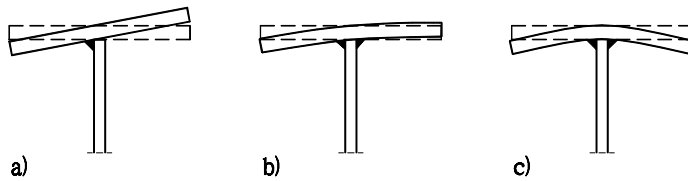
Flanschverformungen durch Schweißverzug
